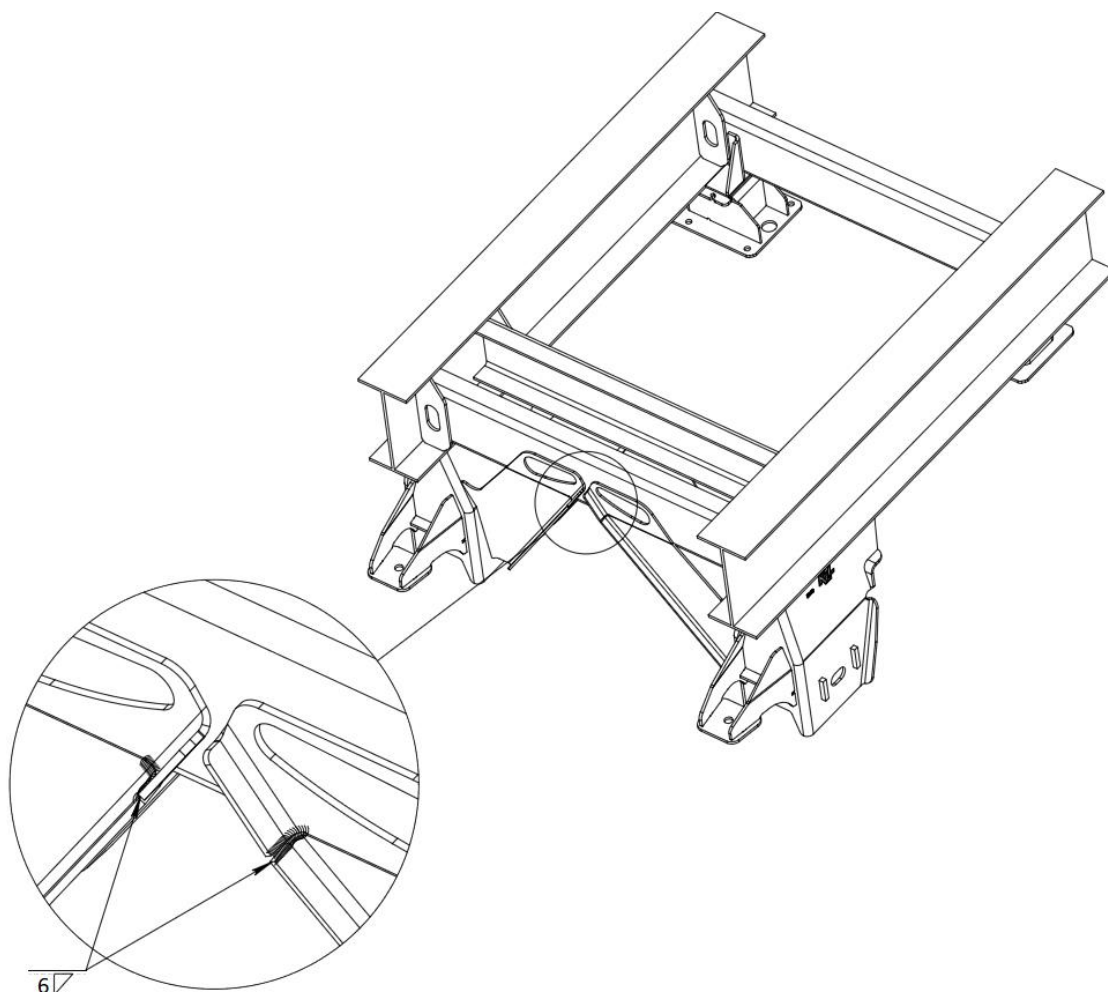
Detalhe de preenchimento de solda dos reforços do suporte frontal
